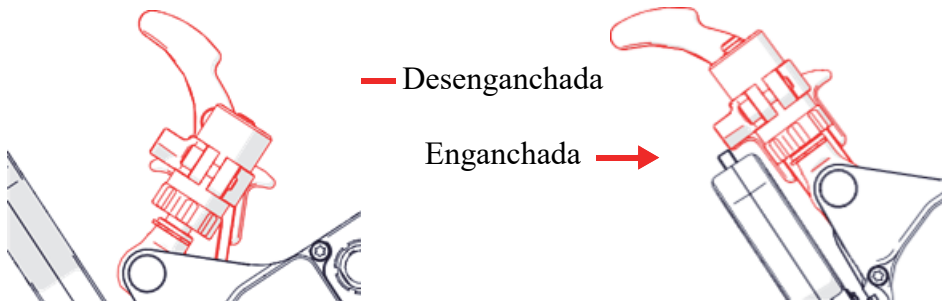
Posiciones de la empuñadura de enganche de motor
